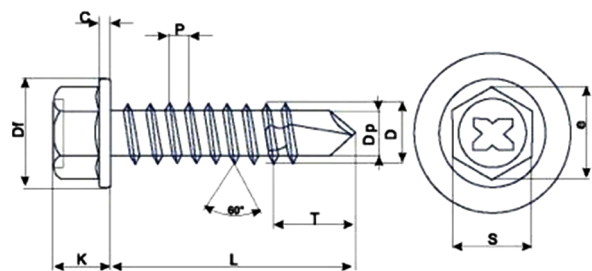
Шуруп-саморіз. Стандарт (група) – DIN 7504K; Матеріал – сталь цементована загартована; Клас міцності – 560HV; Покриття – цинк білий; Модель (марка) – ТЕХ-Н; Голівка – шестигранна; Вид різьблення – повна; Область застосування – по металу
